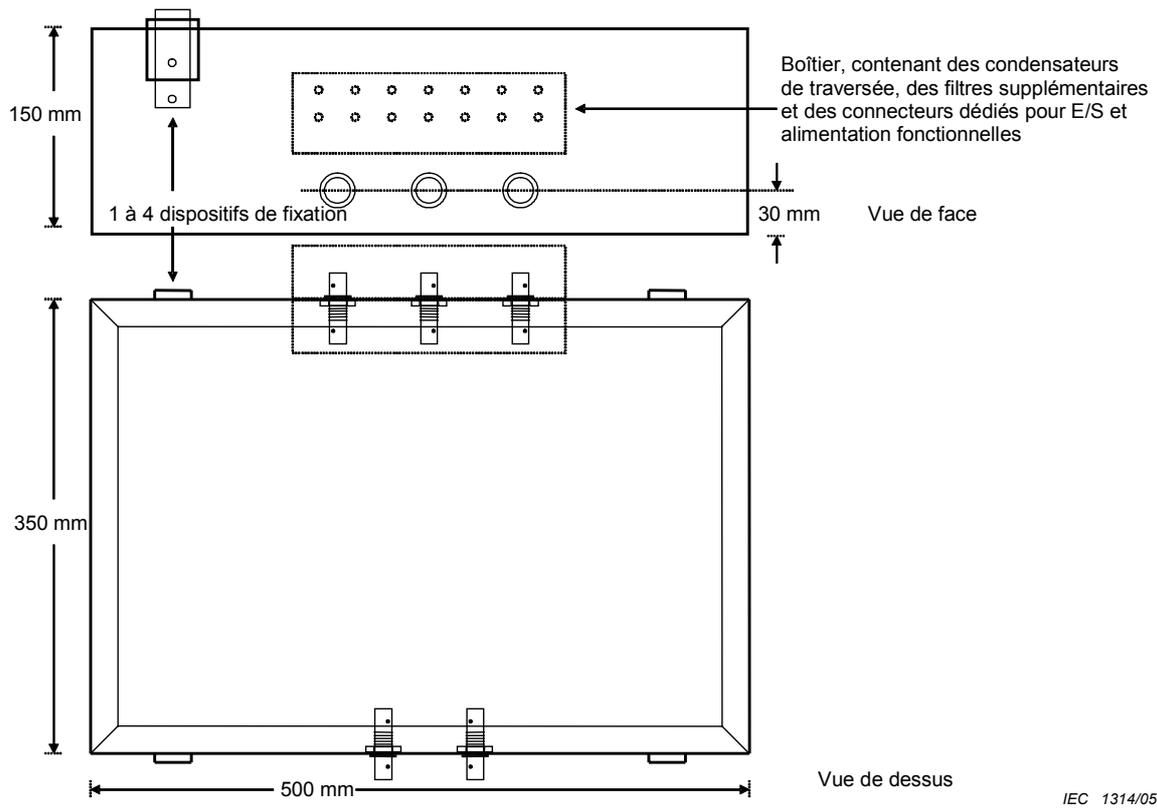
Dessin mécanique de la cage de Faraday sur banc de travail
